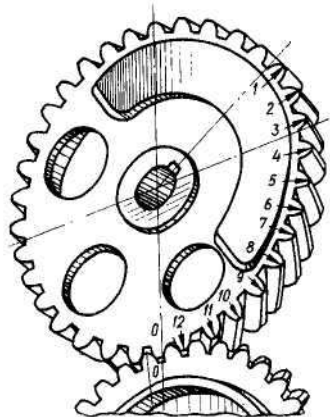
Установочные метки 0 на шестернях балансирного механизма
